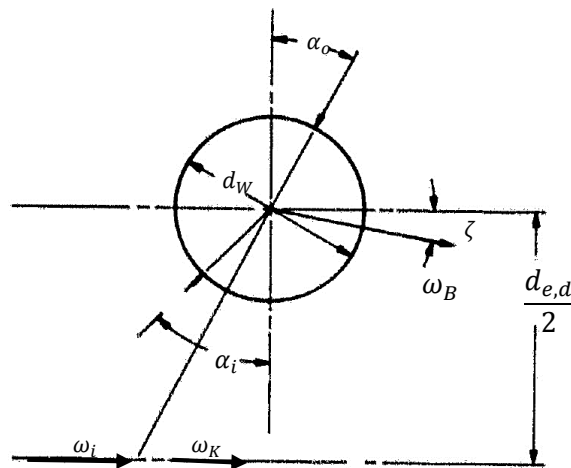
Kinematik eines Wälzkörpers (Hamrock, Ball Bearing Mechanics 1981)
